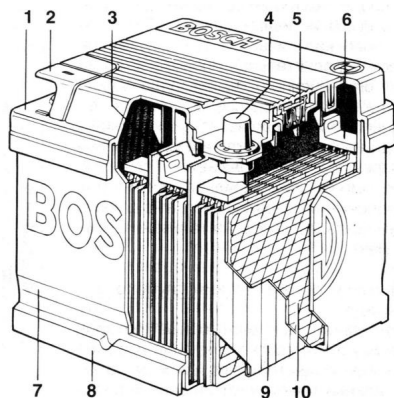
Необслуживаемая аккумуляторная батарея: 1 – неразъемная крышка; 2 – крышка вывода; 3 – межэлементный соединитель; 4 – клемма; 5 – перегородка; 6 – перемычка пластин; 7 – корпус; 8 – нижняя установочная направляющая; 9 – положительные пластины, помещенные внутрь сепараторов; 10 – отрицательные пластины
